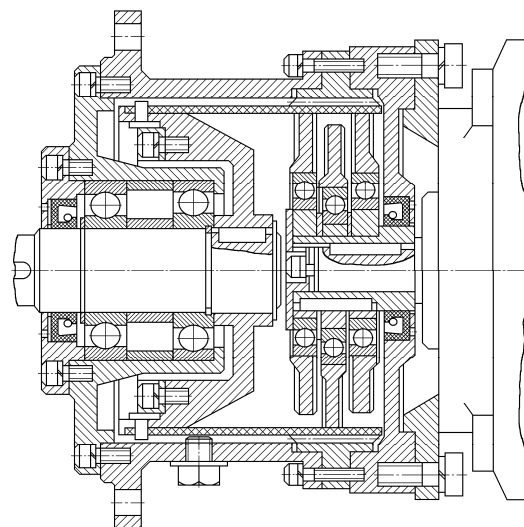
Опытный силовой трехволновой зубчатый редуктор с МГК
